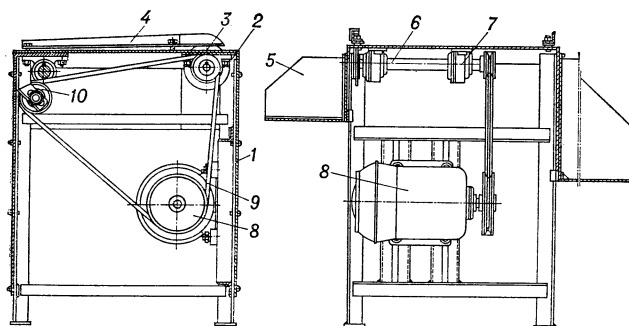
Калибровочная виноградоградная машина: 1 — рама; 2 — стол; 3 — фреза; 4 — калибровочный клин; 5 — бункер; 6 — вал фрезы; 7 — подшипник; 8 — электродвигатель; 9 — клиновидный ремень; 10 — натяжной ролик.
